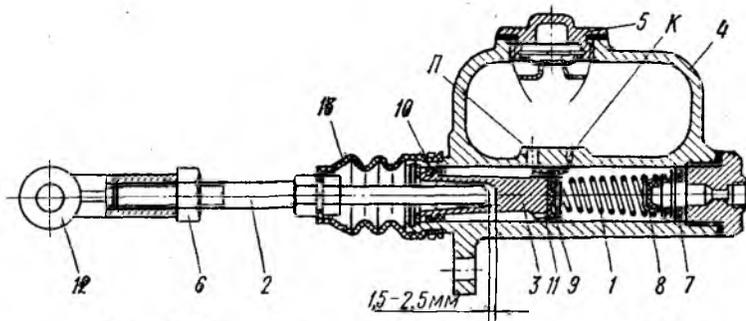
Главный тормозной цилиндр погрузчика КВЗ:
